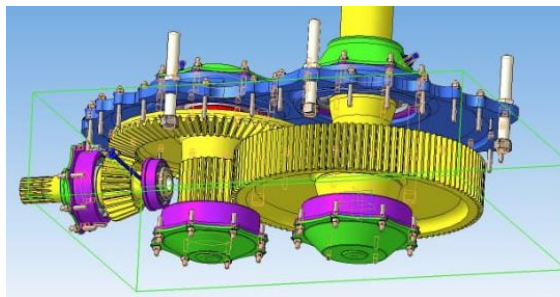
Зубчастий механізм головного редуктора вертольота
